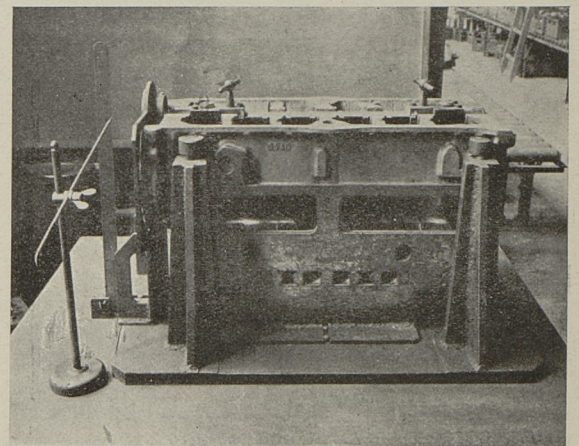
Sprawdzenie w odlewni rdzeni do formy odlewniczej.
